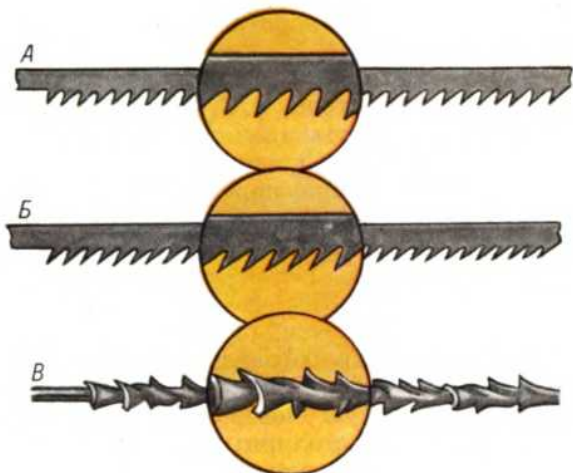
Пилки для лобзиков: А — по дереву; Б — по металлу; В — круглая универсальная для дерева и пластмасс.
